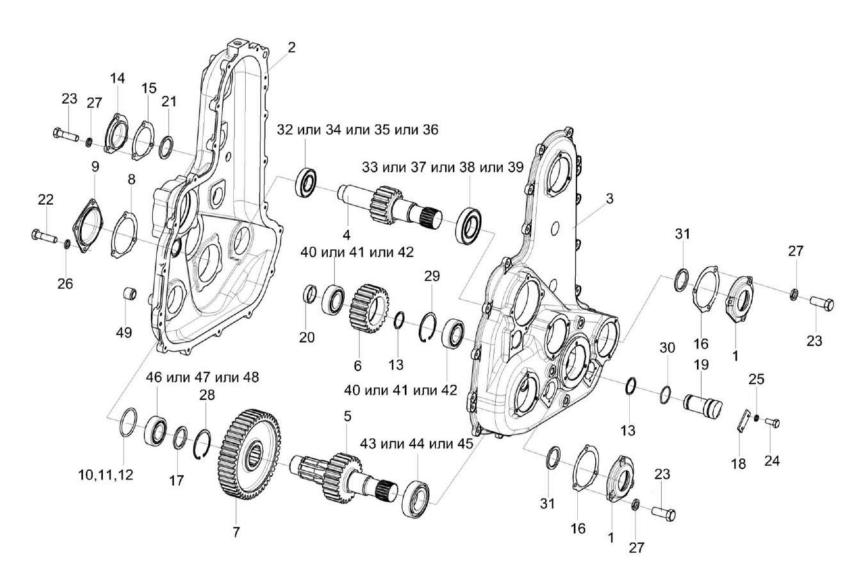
Редуктор КВК 0114100 (лист 3)
